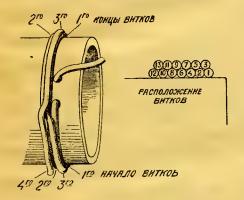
Способ намотки и расположение витков двуслойной катушки.
